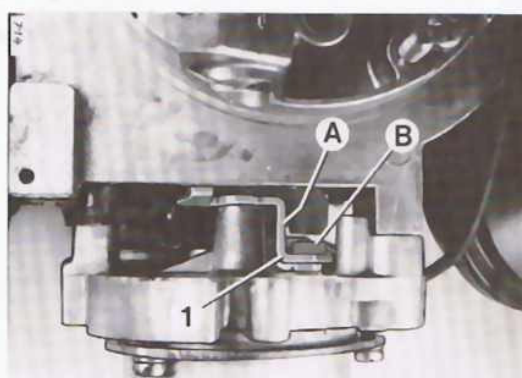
A = Ansatzpunkt für Haltewerkzeug
